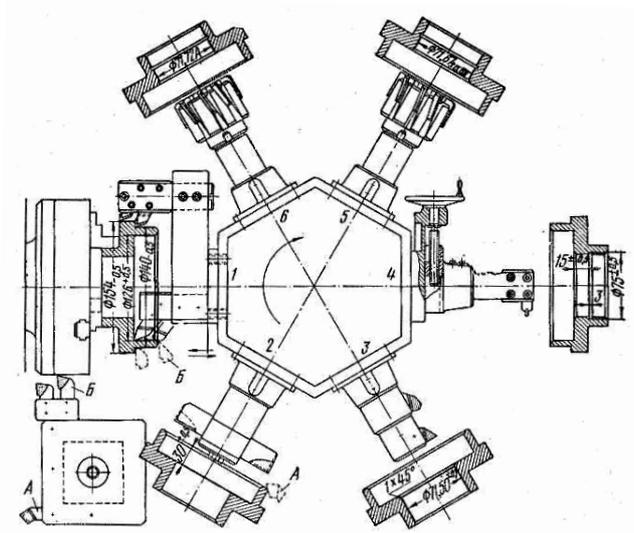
Схема обработки заготовки на токарно-револьверном станке
